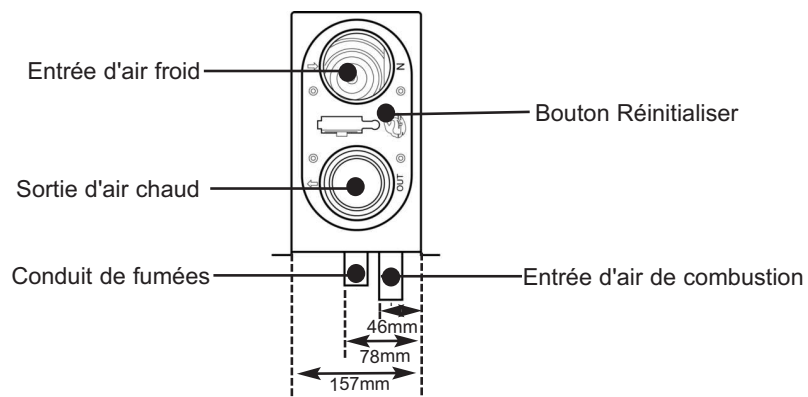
Installation interne - Vue frontale - SH2202 ou SC2202
